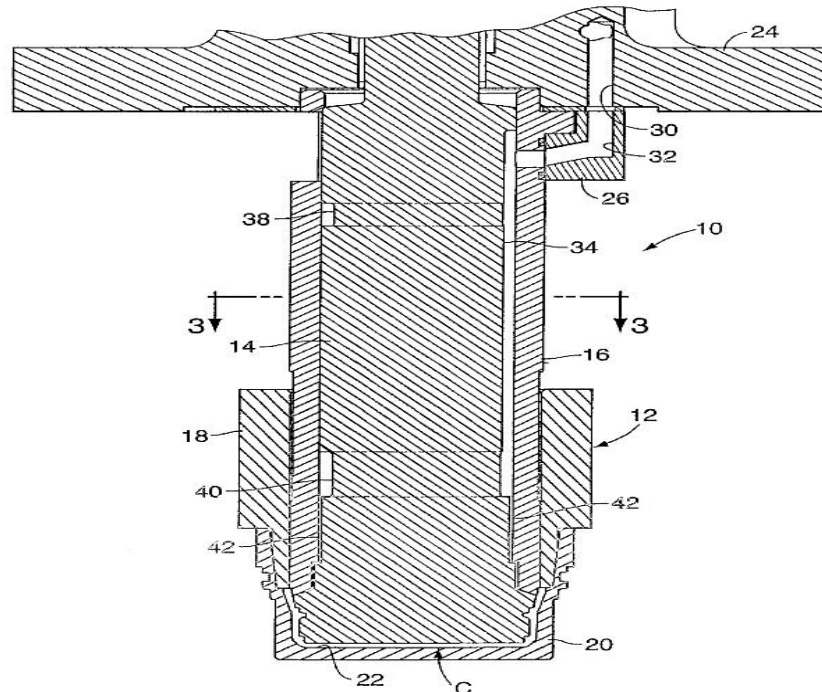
Схема механізму для формування пластмасового закупорювального засобу
